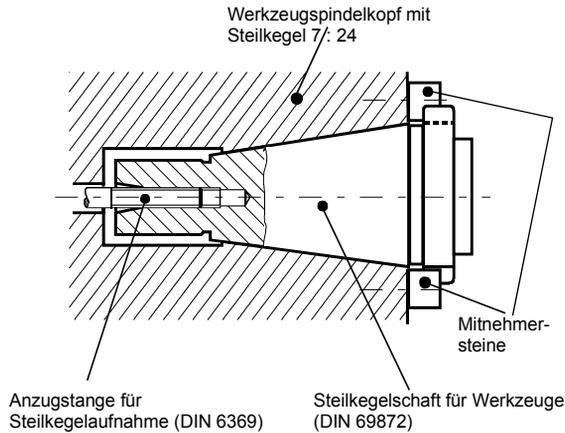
Werkzeugspindelkopf mit Steilkegelschaft 7:24 für Werkzeuge nach DIN 69872/DIN 2080
